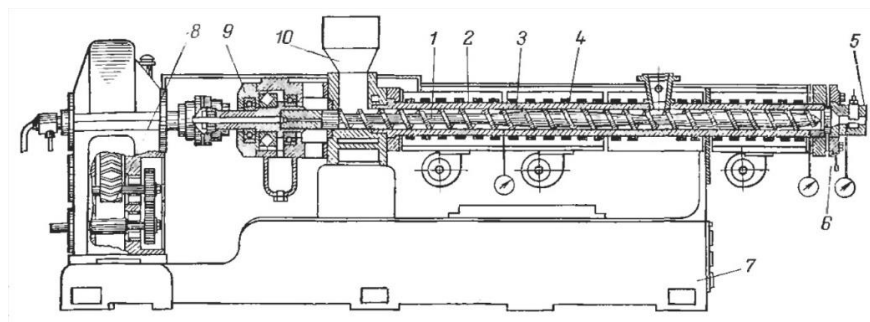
Одношнековый экструдер: 1 – шнек; 2 – корпус; 3 – гильза материального цилиндра; 4 – нагревательные элементы; 5 – экструзионная головка с профилирующим инструментом; 6 – адаптер; 7 – станина; 8, 9 – редуктор и блок упорных подшипников; 10 – бункер
